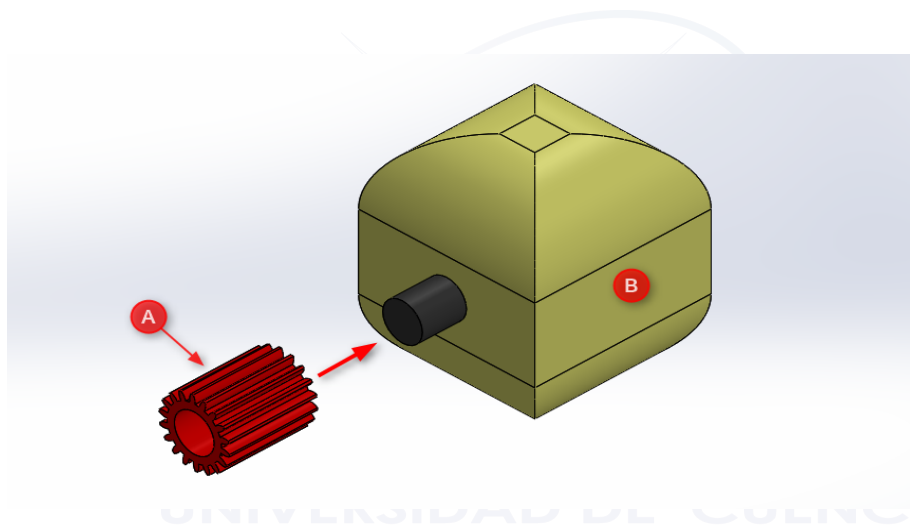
Acoplamiento entre rueda dentada principal A y motor reductor B
